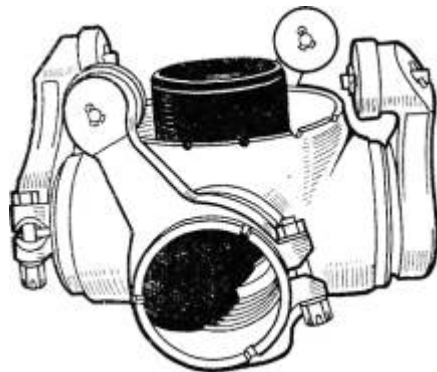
Узел корпуса втулки винта (в собранном виде)
